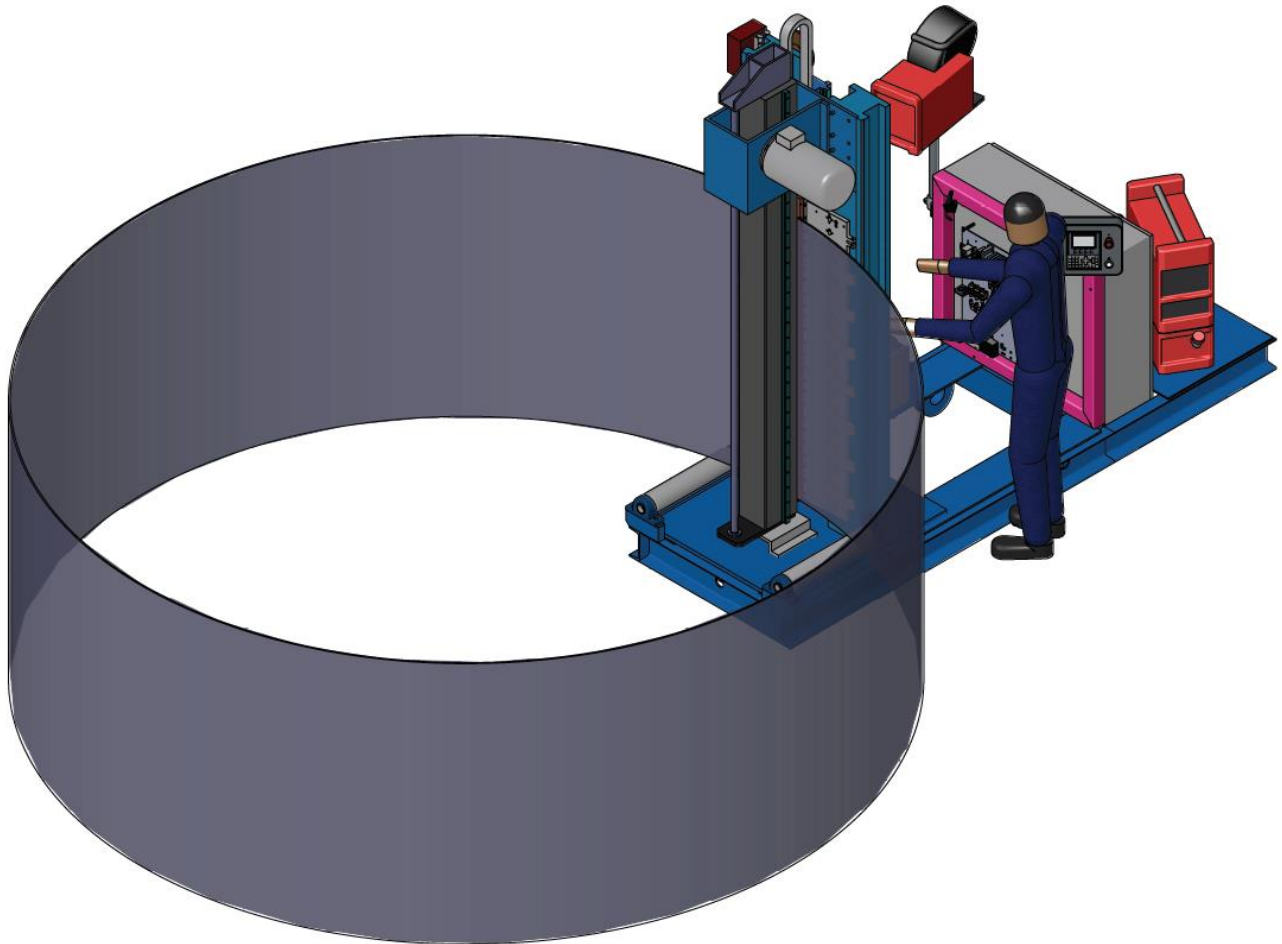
LINEARWELD VTCL 1600 Längsnahtschweißmaschine für stehende Behälterfertigung
